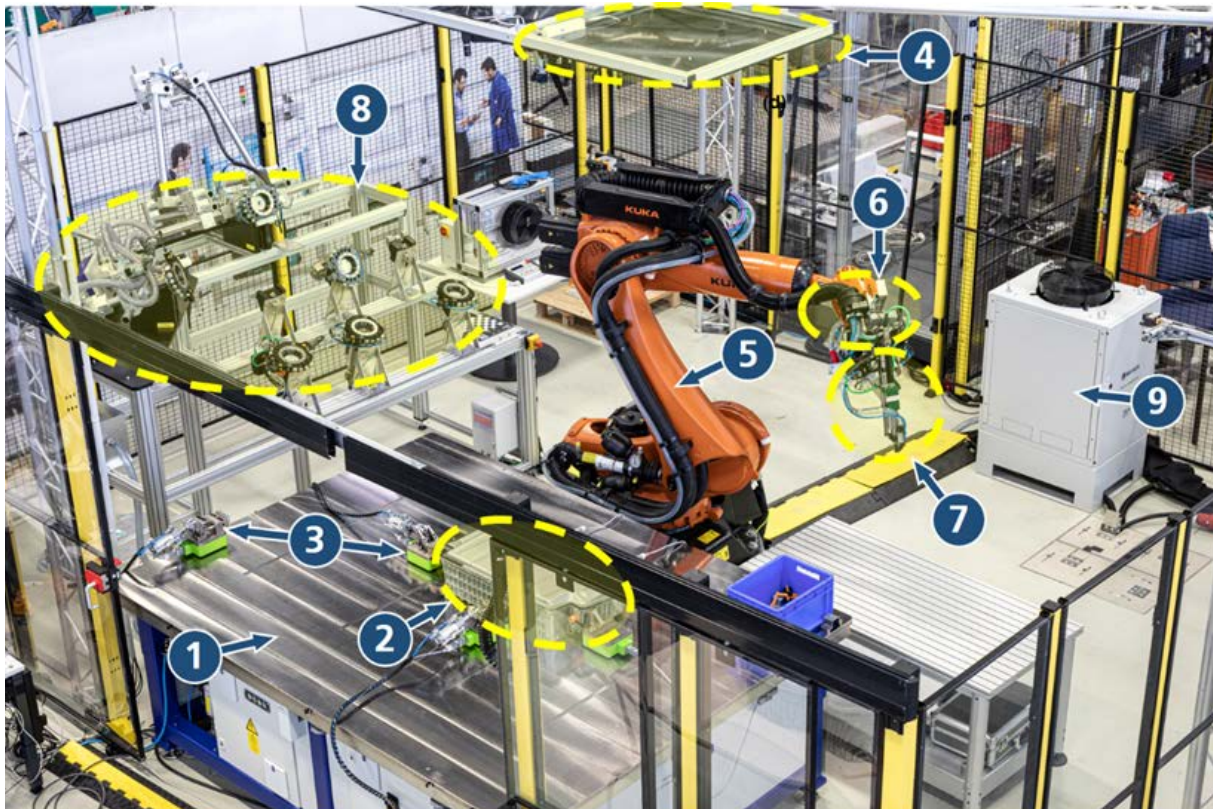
Bestandteile der Demontagestation: (1) Bearbeitungstisch; (2) Batteriesystem; (3) Spannsysteme; (4) Vision-System; (5) Roboter; (6) Kupplungssystem; (7) Einwechselbares Werkzeug; (8) Werkzeugbahnhof; (9) Unterdruckerzeugung.
